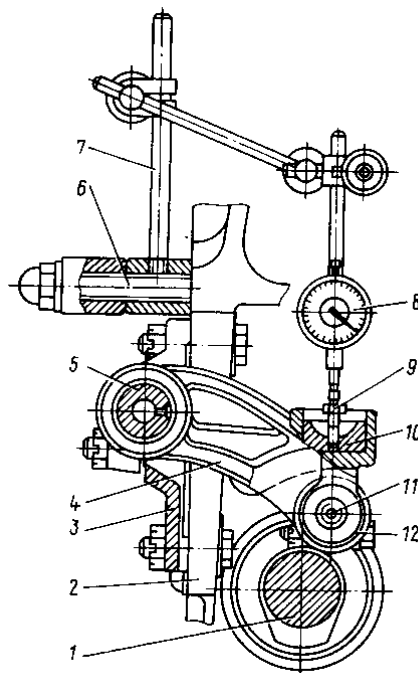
Установка индикатора для проверки фаз газораспределения:
